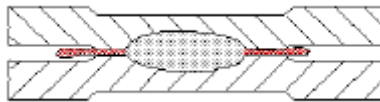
Representação de excesso de material de soldadura
